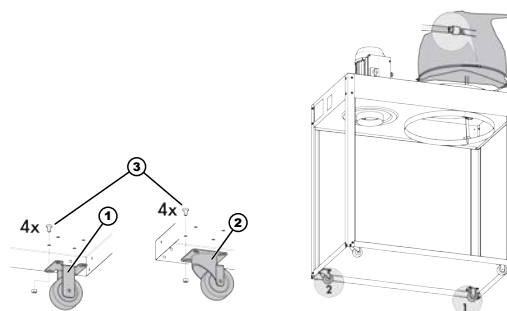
Monter les roulettes pivotantes / roulettes fixes
